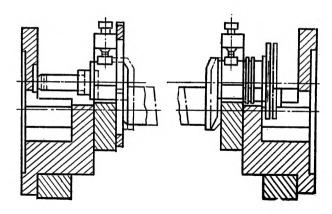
Положение коленчатого вала в патронах станка при шлифовании в жестких центросместителях.
